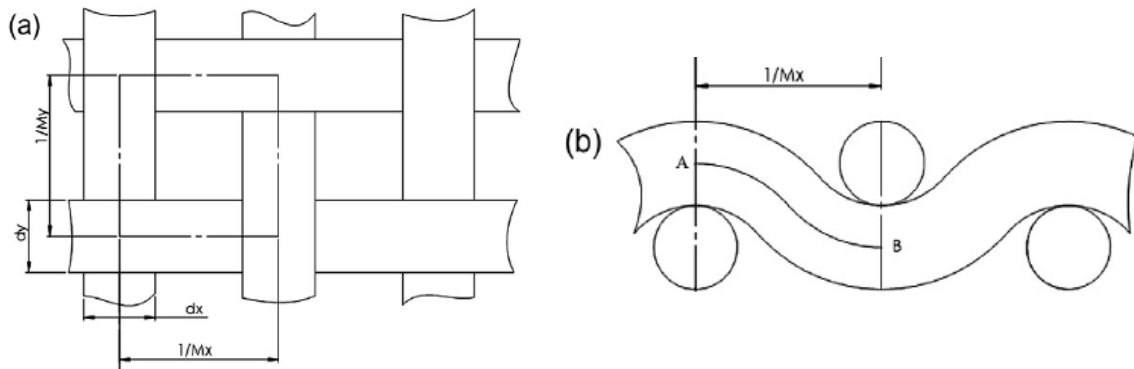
Malla de hilo metálico rectangular. a) Vista en planta; b) Vista frontal. Fuente: [186]
